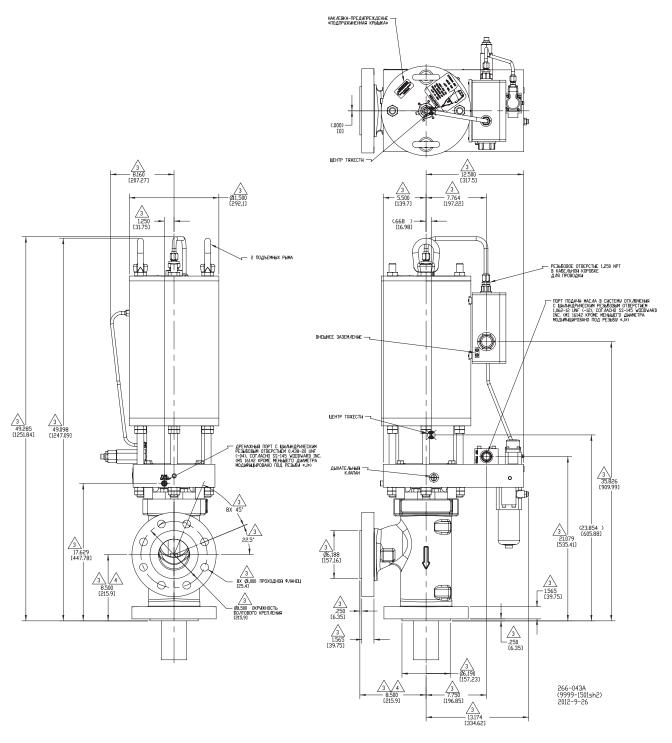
Габаритный чертеж регулятора SonicFlo (4 дюйма, класс 600)
